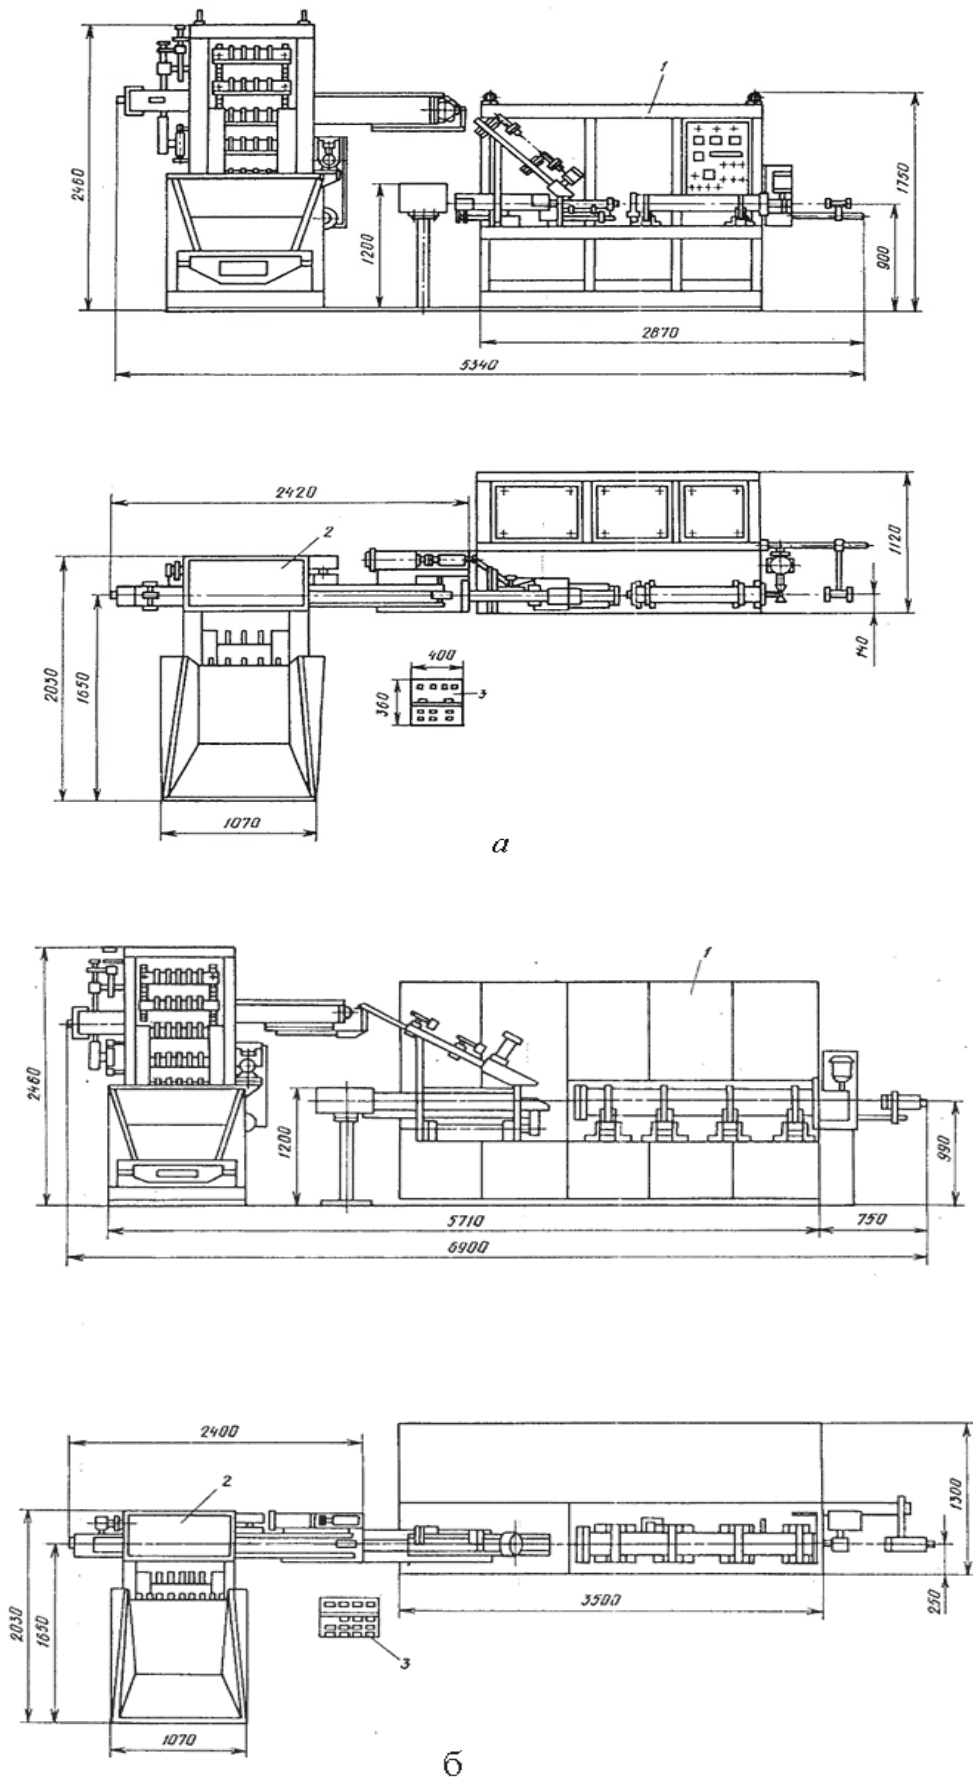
Схема автоматической линии для индукционного нагрева заготовок под штамповку мощностью 250 кВт (а) и 500 кВт (б): 1 – нагреватель индукционный; 2 – автоматизированное загрузочное устройство; 3 – пульт управления
